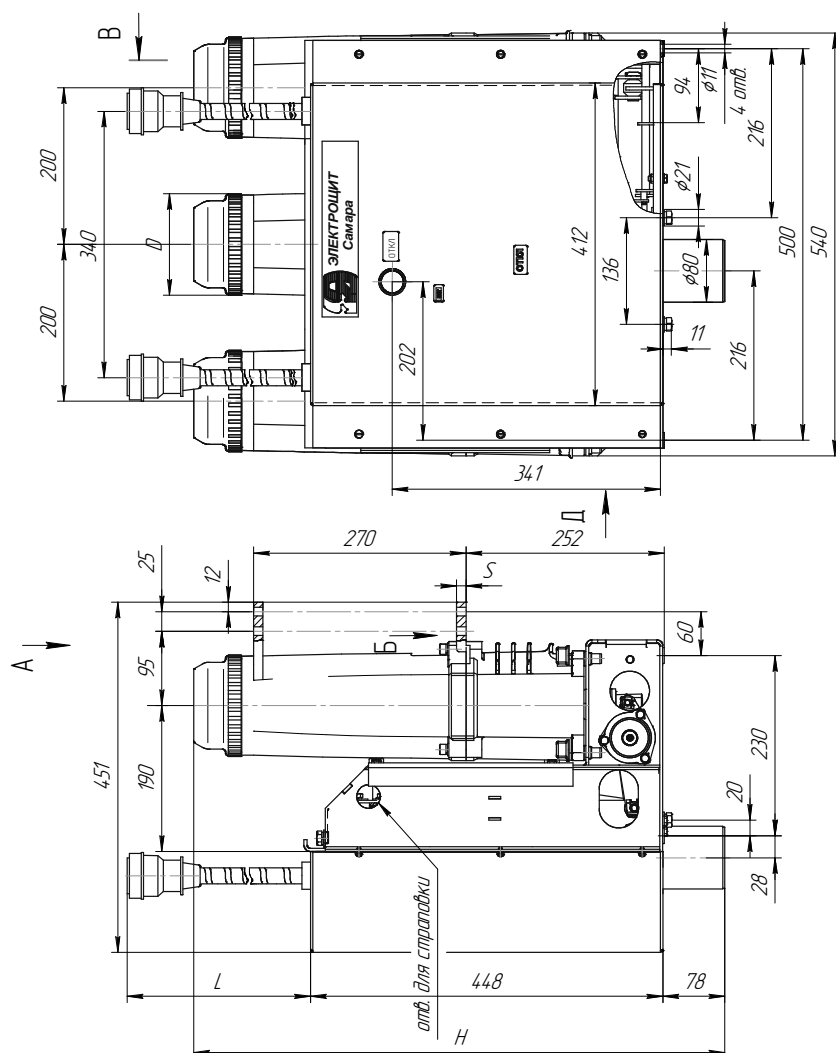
Габаритные, присоединительные и установочные размеры выключателя типа ВВУ-СЭЩ-ЭЗ-10-20(31,5)/
